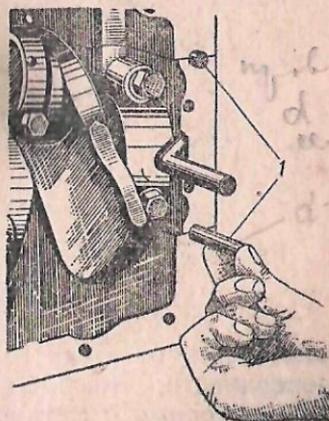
Установка сальников между картером и крышкой заднего коренного подшипника:
